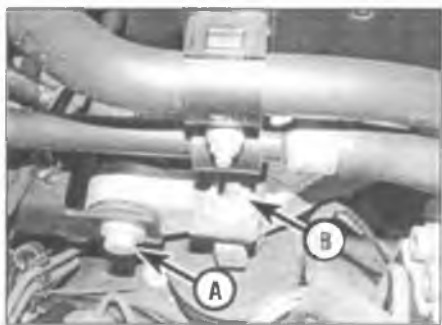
Отсоедините верхнюю стяжку (А) и отверните гайку опоры двигателя (В)
